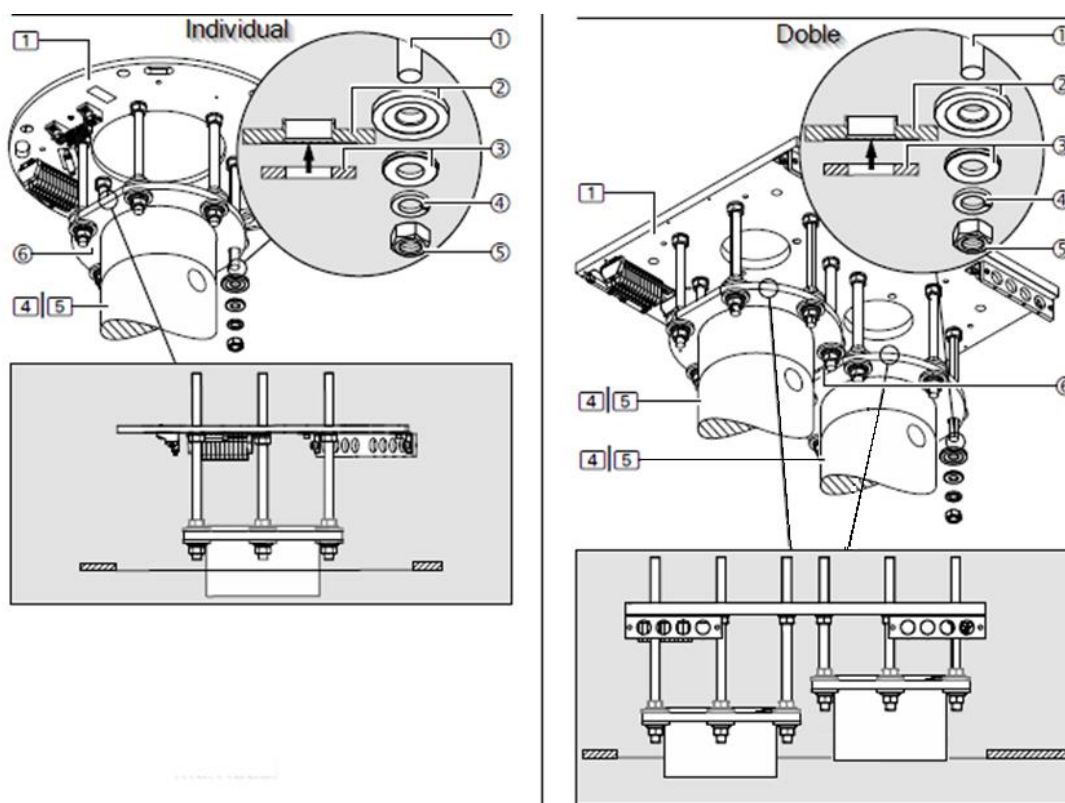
Montage de la bride du tube de toit sur les boulons filetés
